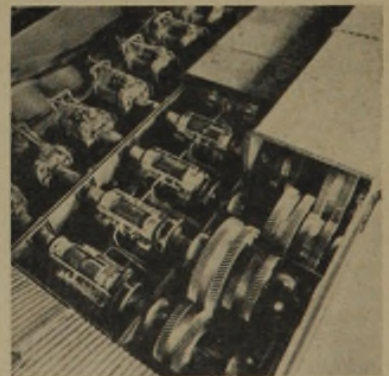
Getriebe- und Kammwalze einer Drahtstraße
